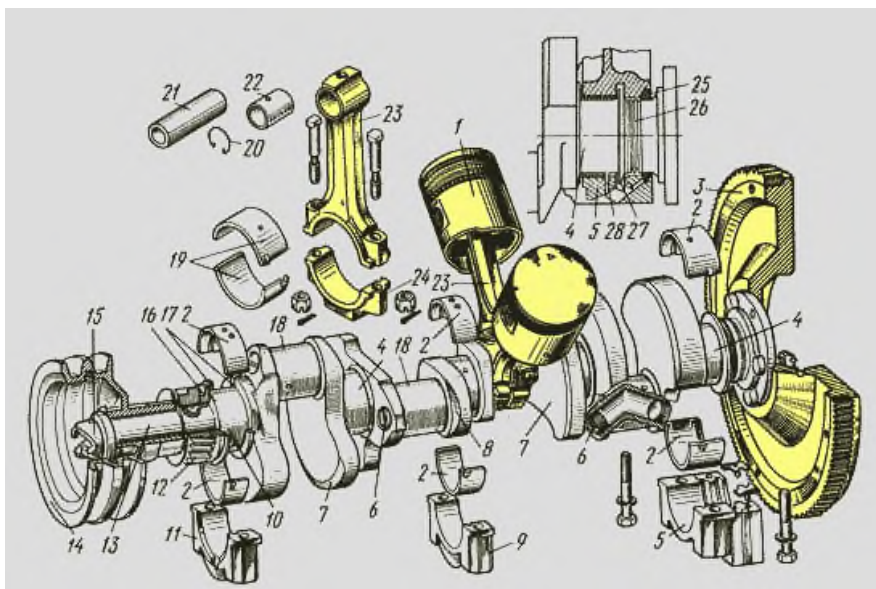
Детали кривошипно-шатунного механизма двигателя
